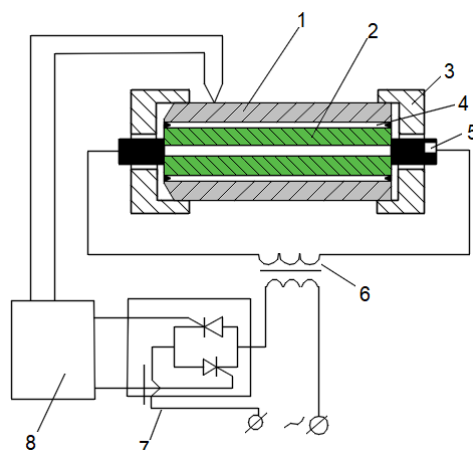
Схема градиентного нагрева биметаллической заготовки электроконтактным способом: 1 – 1201; 2 – ВТ6с; 3 – фиксаторы; 4 – вакуумированный зазор между компонентами; 5 – система токоподвода; 6 – силовой трансформатор; 7 – блок тиристоров; 8 – блок управления
